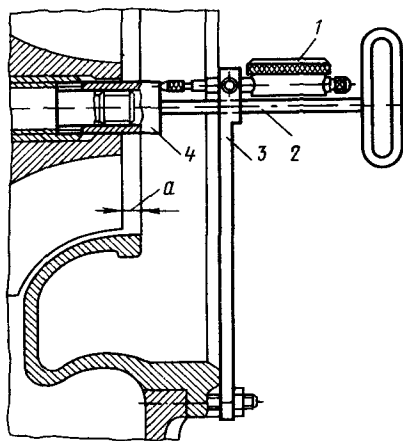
Приспособление для проверки зазора между колесом воздухонагнетателя и крышкой корпуса
